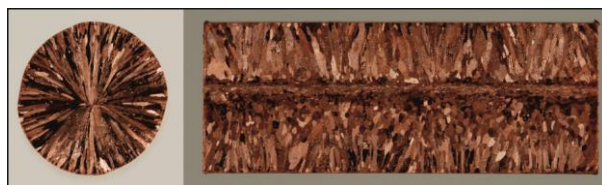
Makrostruktura przekroju poprzecznego i wzdłużnego pręta z miedzi w gatunku Cu-OFE uzyskanego w procesie ciągłego odlewania w warunkach przemysłowych na instalacji Upcast przy prędkości odlewania 3,0 m/min. oraz przy przepływie medium chłodzącego krystalizator wynoszącym 60 l/min.
